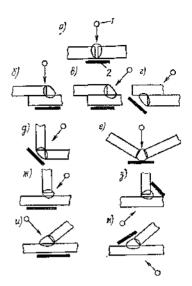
Типовые схемы просвечивания сварных соединений (а-к)
